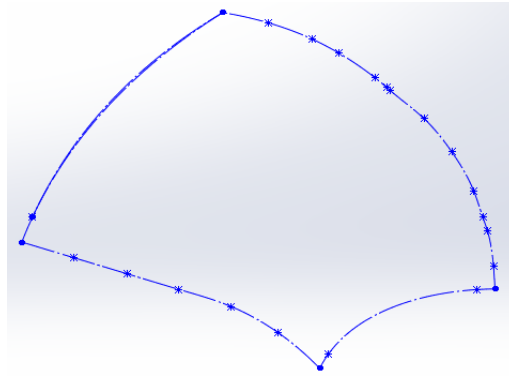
Projeção no plano xy com as arestas de entrada e saída da pá.
